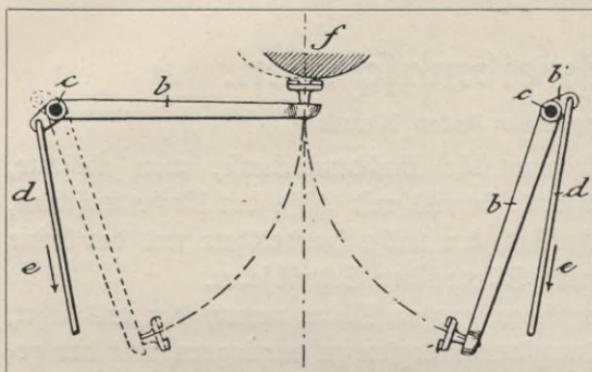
Typenhebel der Remington-Schreibmaschine.
